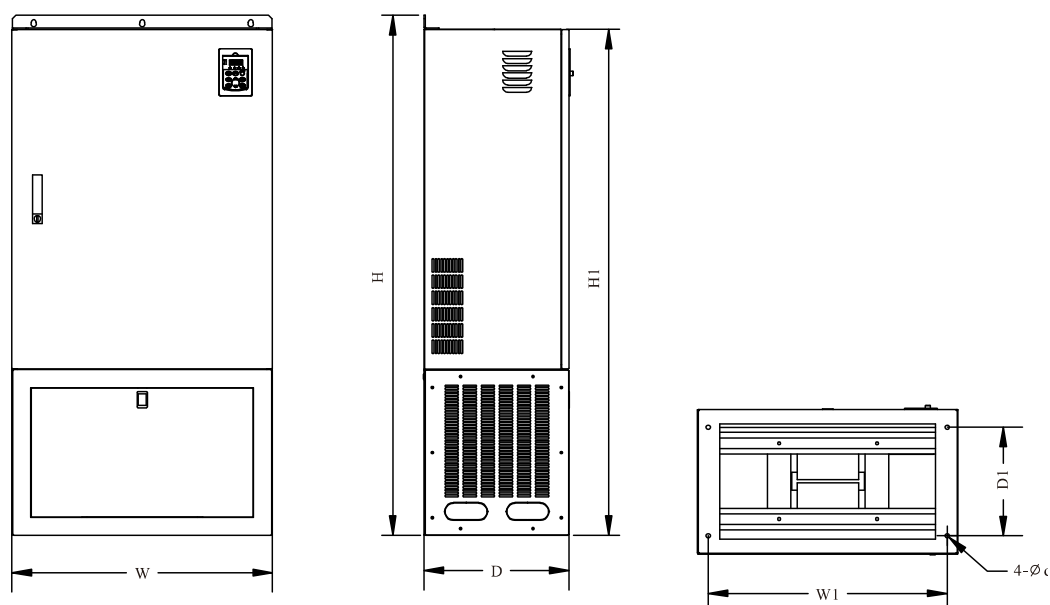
Внешний вид инвертора SL9 шкафного исполнения
